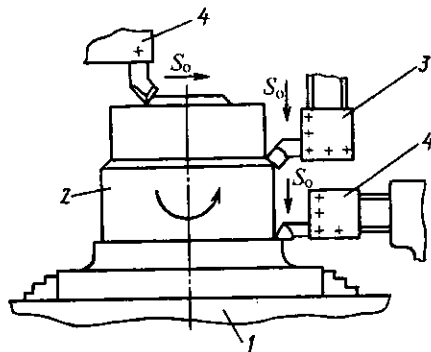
Схема обработки заготовки на токарно-карусельном станке:
